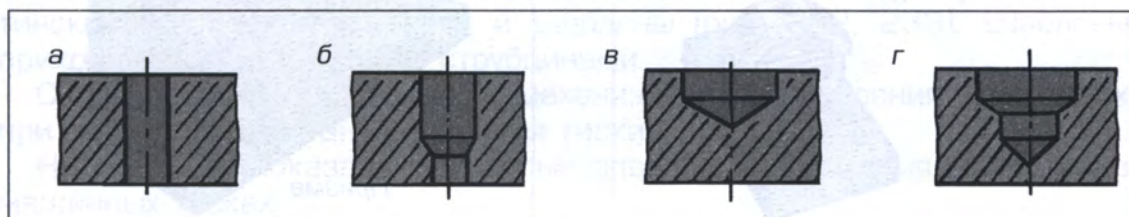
Виды отверстий, выполняемых на сверлильном станке:
